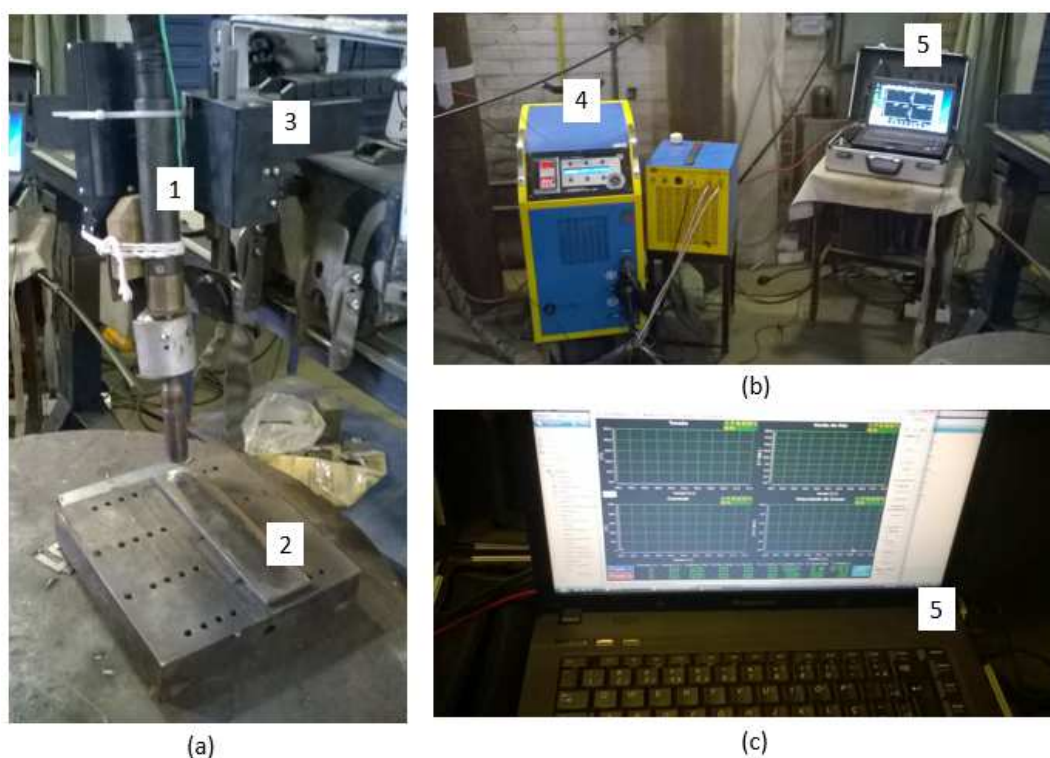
Tocha de soldagem, Tartílope e metal base (a); Fonte de Soldagem e sistema de aquisição (b); em detalhes o sistema de aquisição (c).
